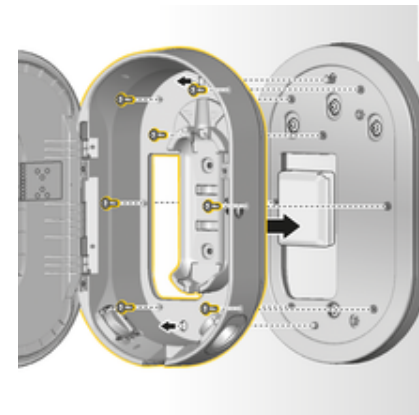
Atornillado del puerto de carga en la placa de montaje
